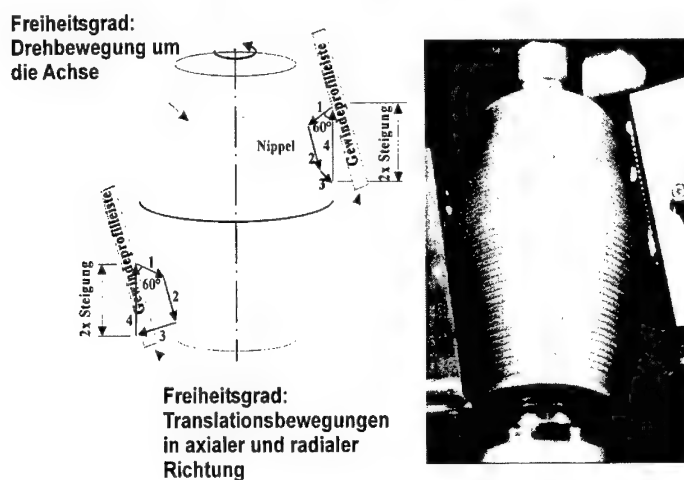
Prinzip der Gewindeerzeugung des Nippels (Quelle: [SGL-99])
